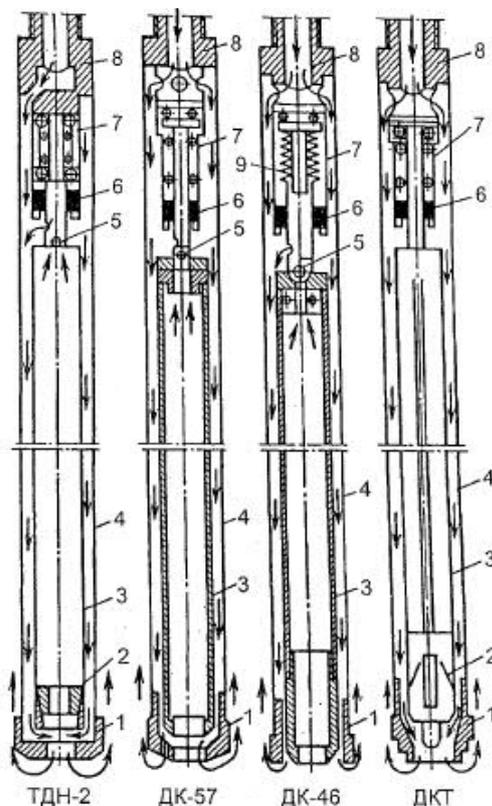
Схемы устройства ДКС с невращающимся при бурении керноприемником: 1— коронка; 2 кернорватель; 3— внутренняя труба (керноприемник); 4— наружная труба; 5— шаровой клапан; 6— сальник; 7 — узел подвески; 8— переходник; 9 — пружина.
